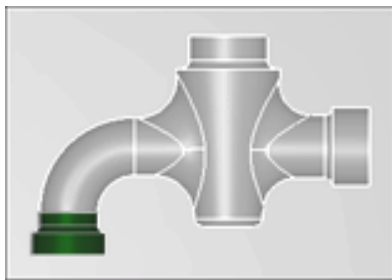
Схема вибору поверхонь фрезерування
